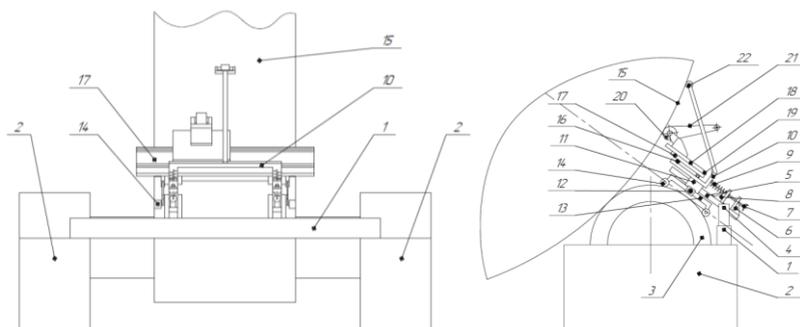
Конструкция предложенного станка для обработки крупногабаритных деталей вращения: 1 - монтажная рама, 2 - корпус подшипника, 3 - опорный ролик, 4 - шарнир, 5 - поперечные профильные направляющие, 6 - неподвижная пятка, 7 - регулировочный винт, 8 - подвижный упор, 9 - пружина, 10 - кронштейн, 11 - корпус, 12 - шарнир, 13 - подвижная роликовая опора, 14 - ролики, 15 – обрабатываемая поверхность, 16 - сдвоенные продольные рельсовые направляющие качения, 17 - продольный суппорт, 18 - каретка, 19 - регулировочный винт, 20 - обрабатывающий узел, 21 - абразивная лента, 22 - копирующий ролик.
